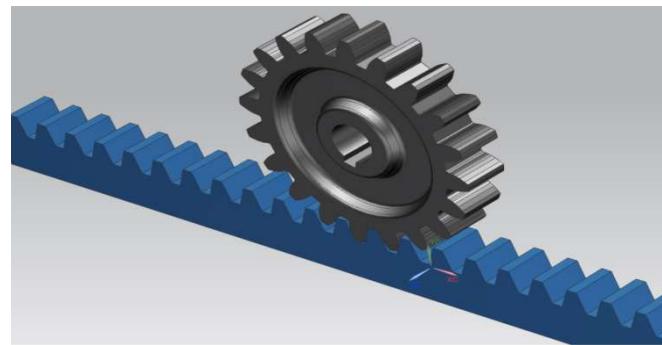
Diseño CAD y ensamblaje de piñón-cremallera.
